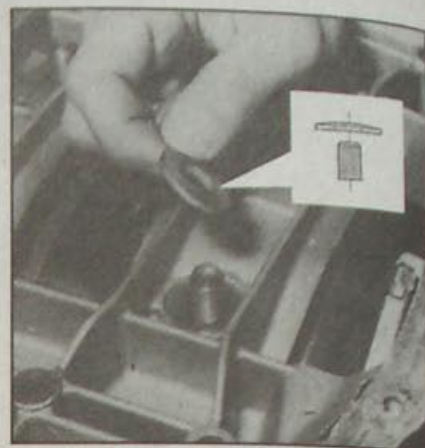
Установка специальной шайбы для гайки крепления крышки коренного подшипника выпуклой поверхностью в сторону гайки
